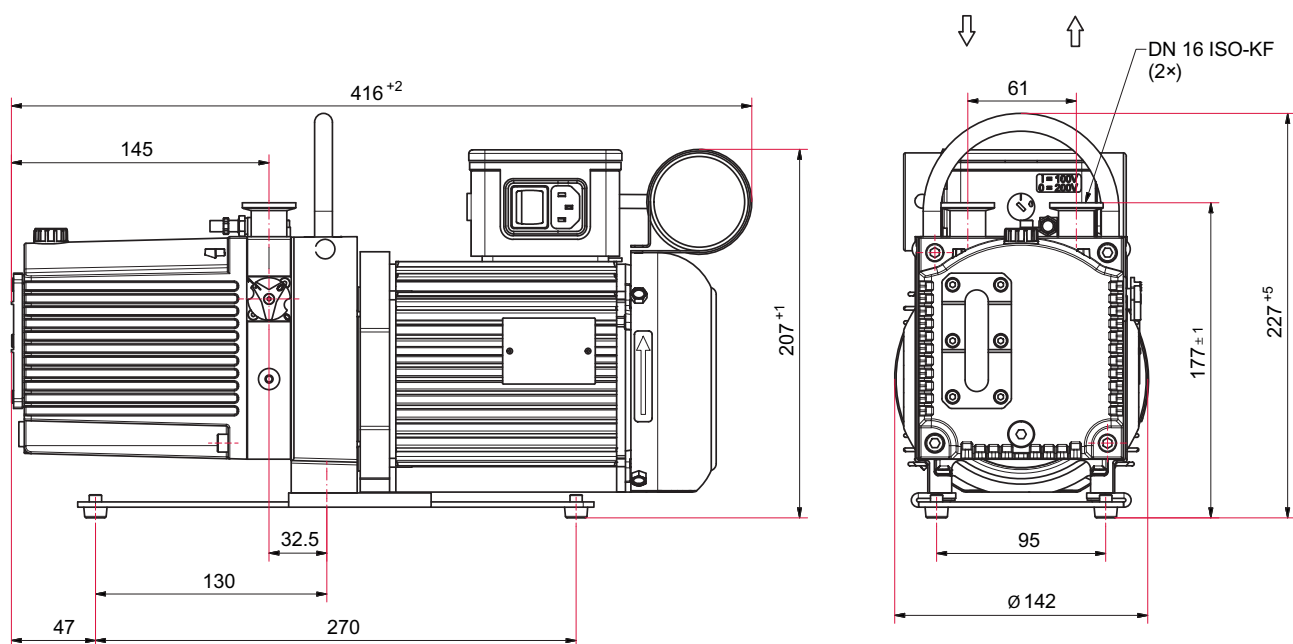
Dimensões do Duo 6, motor monofásico, 100/200 V, 50/60 Hz
